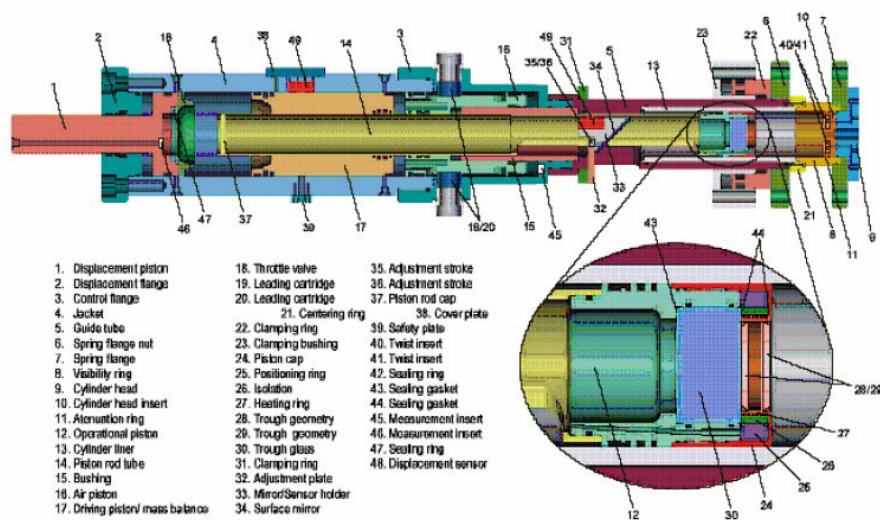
Máquina de compresión rápida. Adaptada de [82]
